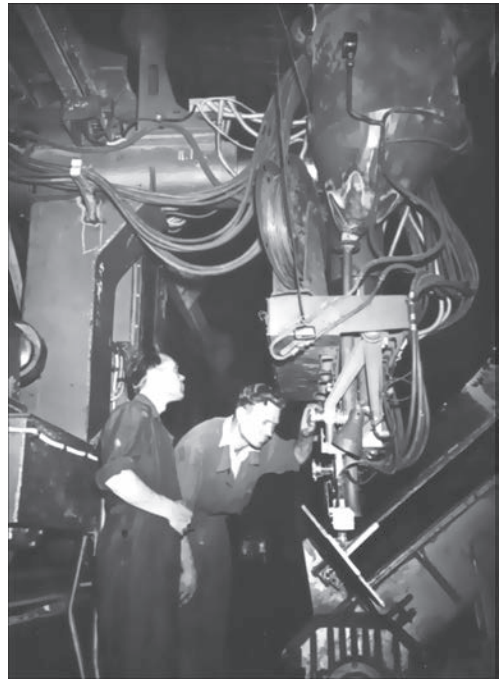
Устаткування для автоматичного зварювання корабельних конструкцій
